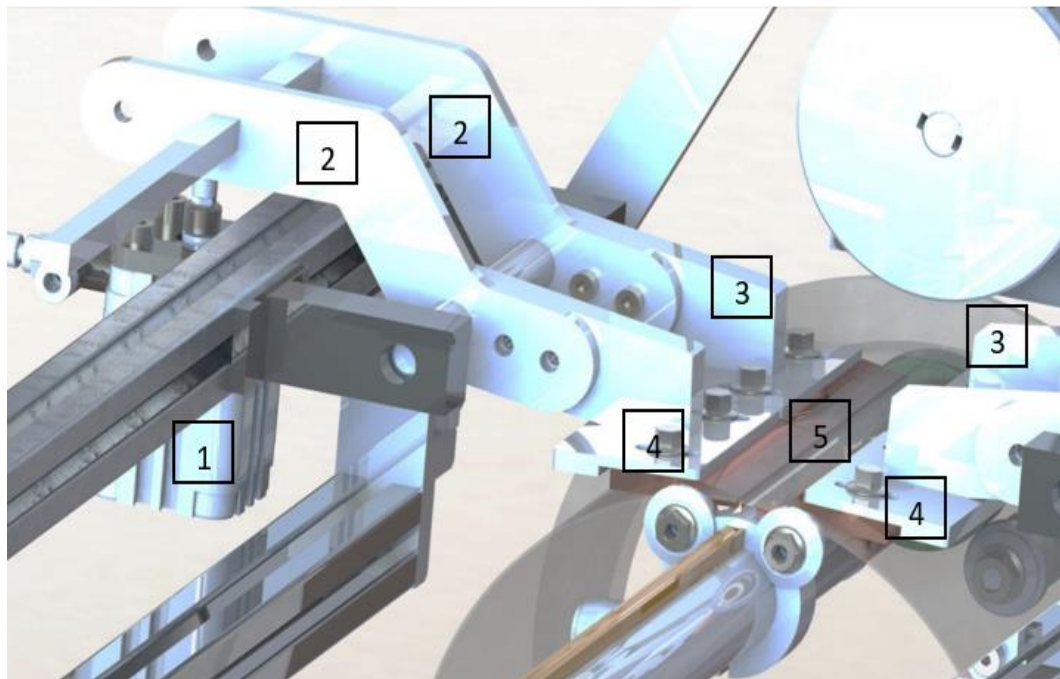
Partes que integran el sistema de sujeción por mordaza para soldadura lineal de la tubería.
